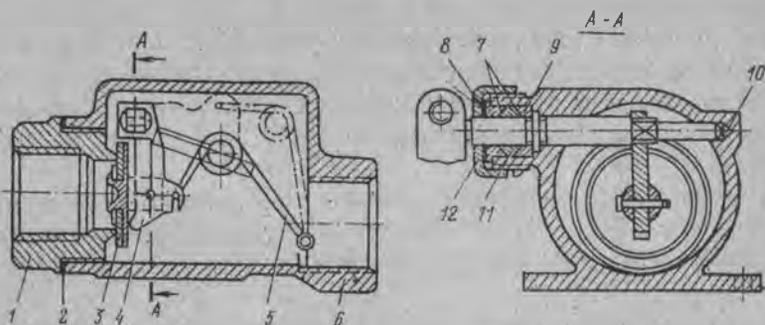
Перекрывной кран 630600К: 1 — штуцер; 2 — уплотнительное кольцо; 3 — тарелка; 4 — рычаг; 5 — пружина; 6 — корпус; 7 — втулка; 8 — уплотнение; 9 — вкладыш; 10 — ось; 11 — фасонное кольцо; 12 — гайка
